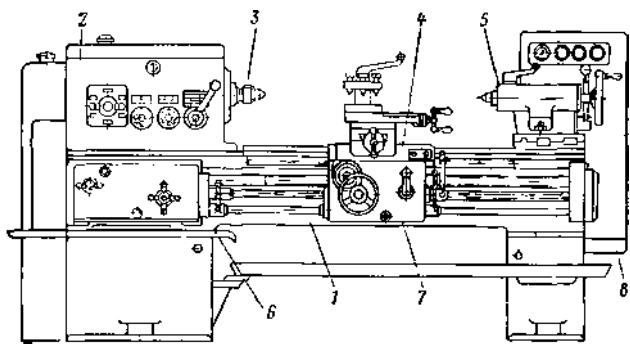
Общий вид токарно-винторезного станка модели 1К62Б.
